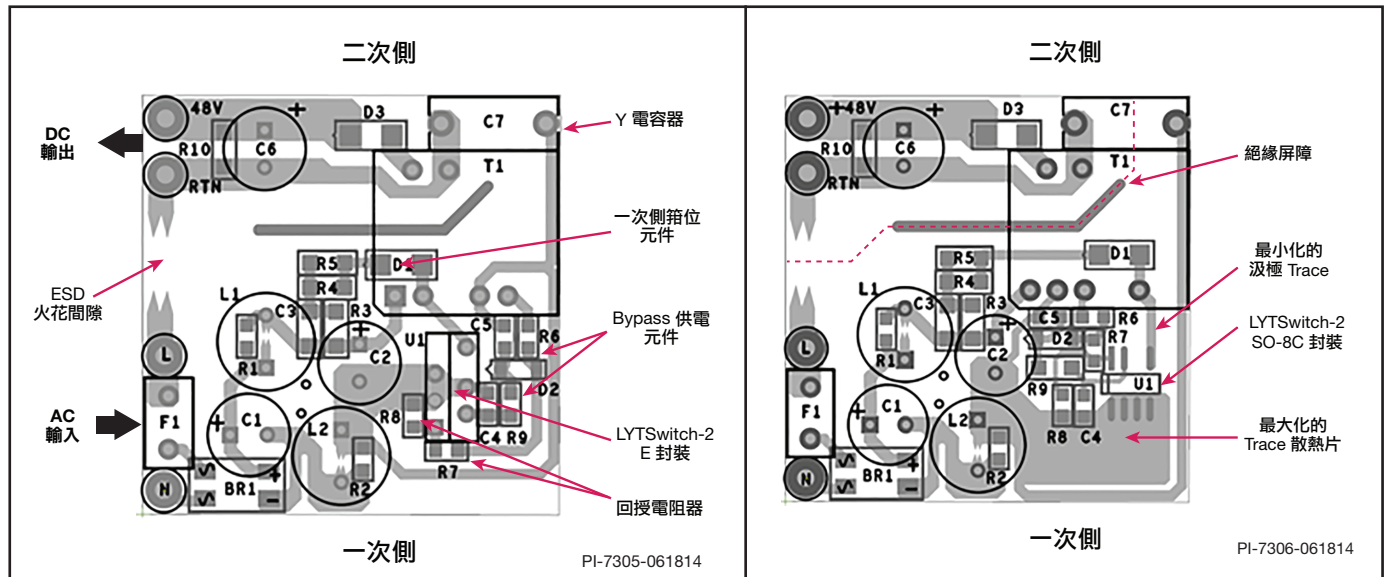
使用 eSIP 封裝的 PCB 佈局範例
